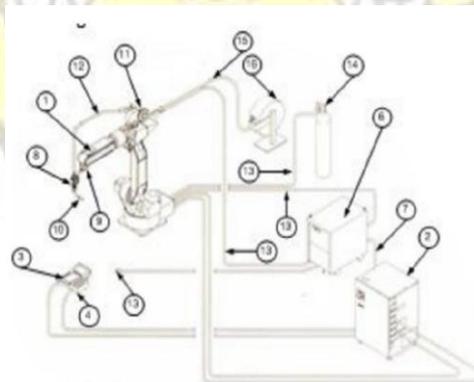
Arc Welding Robot Tipe Almega AX– V6
